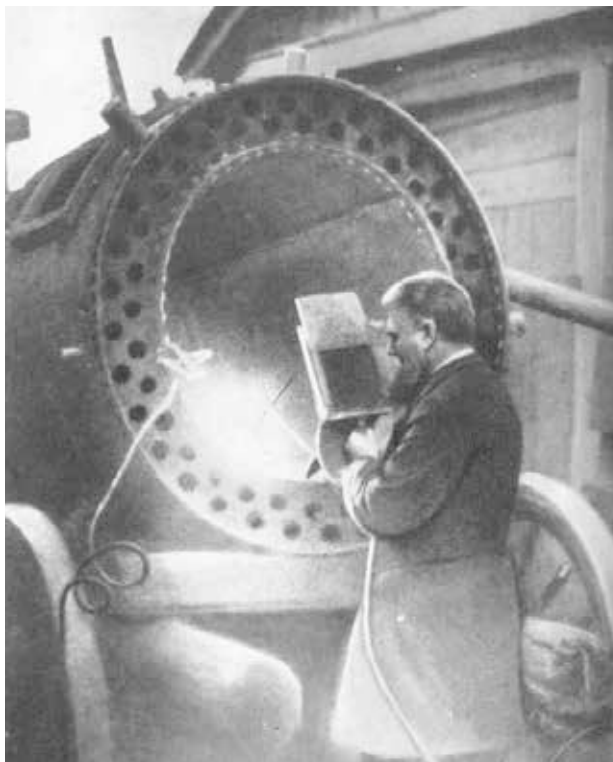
Н. Н. Бенардос за сваркой котла [6]
